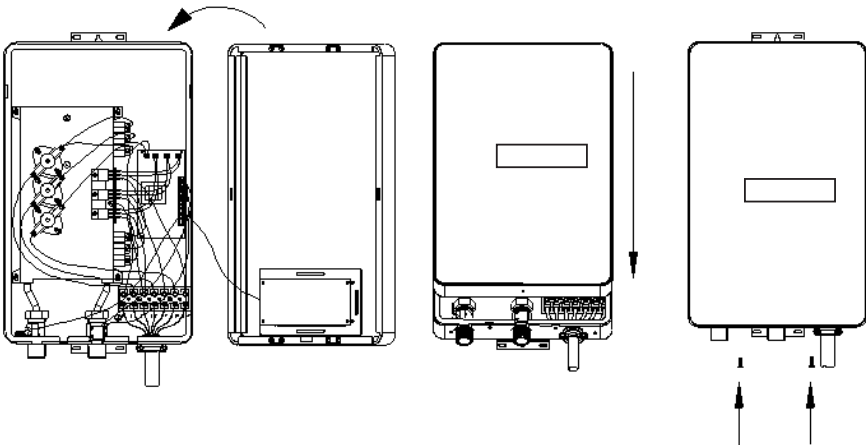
Vuelva a conectar el cable plano de del panel LCD si está desconectado y reinstale la cubierta frontal con los tornillos y arandelas que quitó anteriormente.
